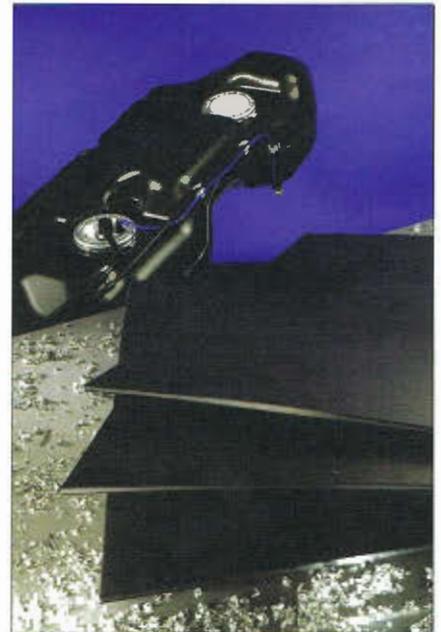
Tanque de gasolina feito por termoformação e soldagem de chapas de PE com múltiplas camadas e boas propriedades de barreira produzidas pela Simona
